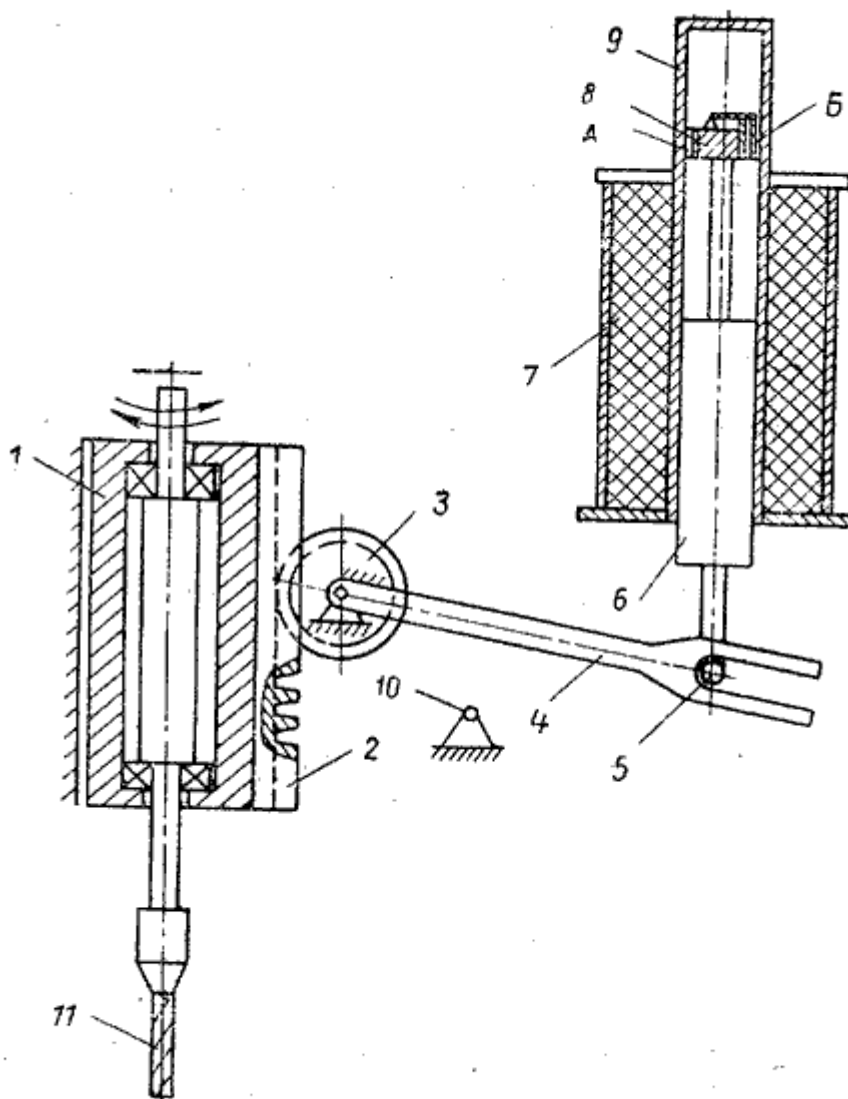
Привод подачі шпинделя свердлильного верстата. [14]
